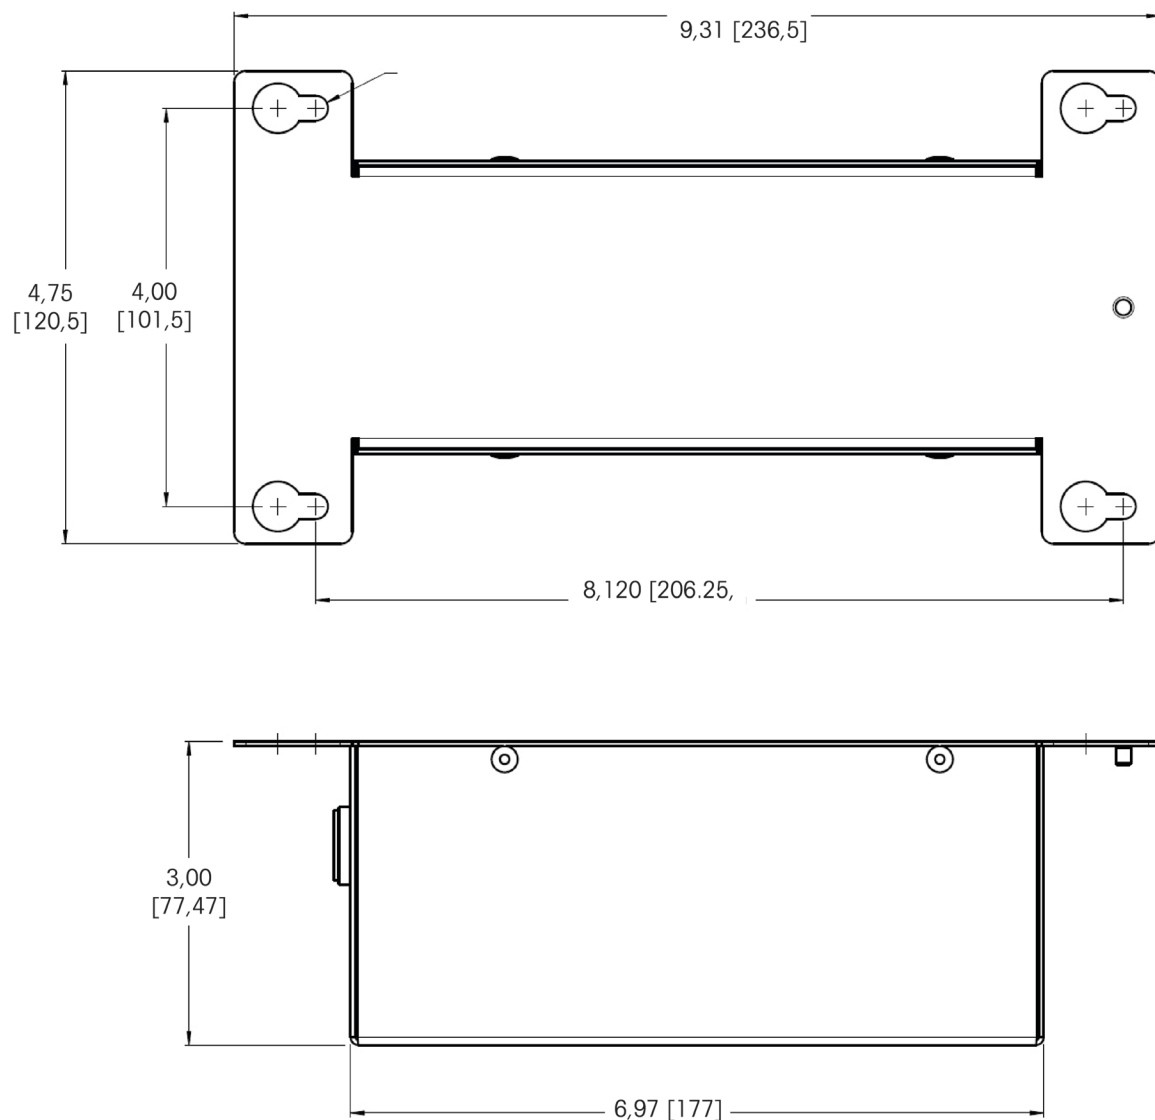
Dimensions générales du bloc de batteries 30538111
